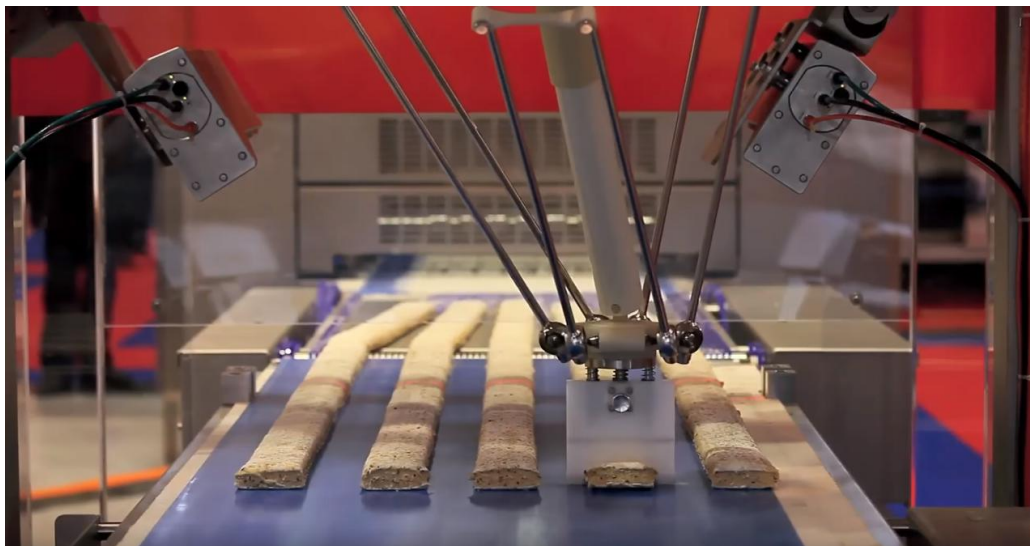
Laser Engraving Delta Robot [36]
